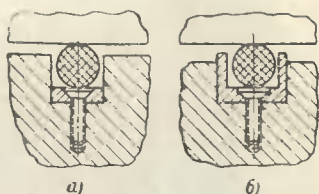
Установка заполнителей для резиновых уплотняющих колец.
